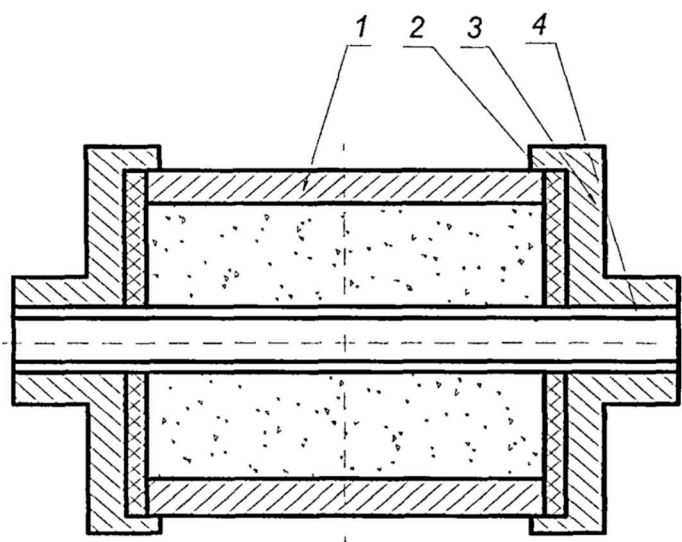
Схема оправки для відцентрового заливання: 1 - заготовка-основа; 2 - прокладки; 3 - фланець; 4 - графітова втулка
